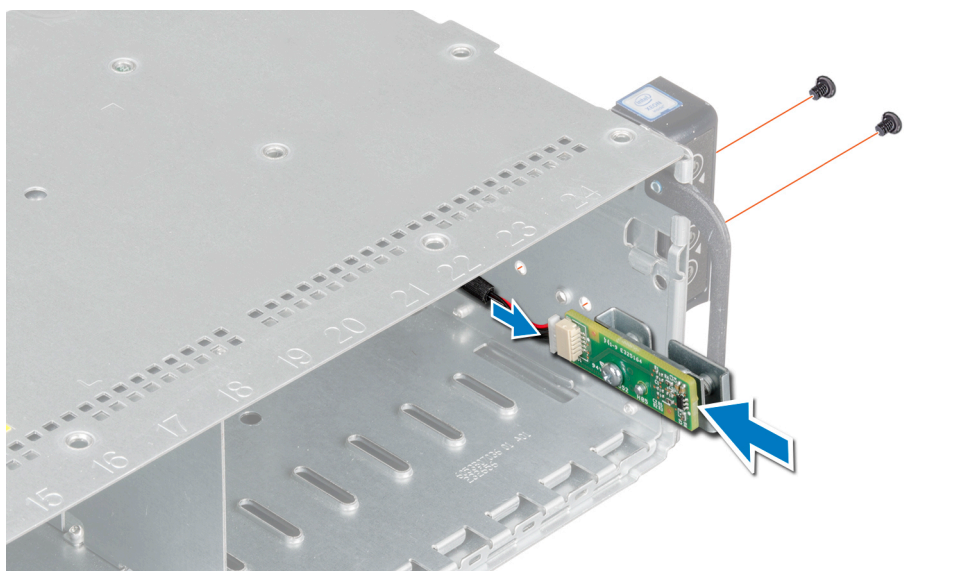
Instalación del ensamblaje de la placa del sensor
